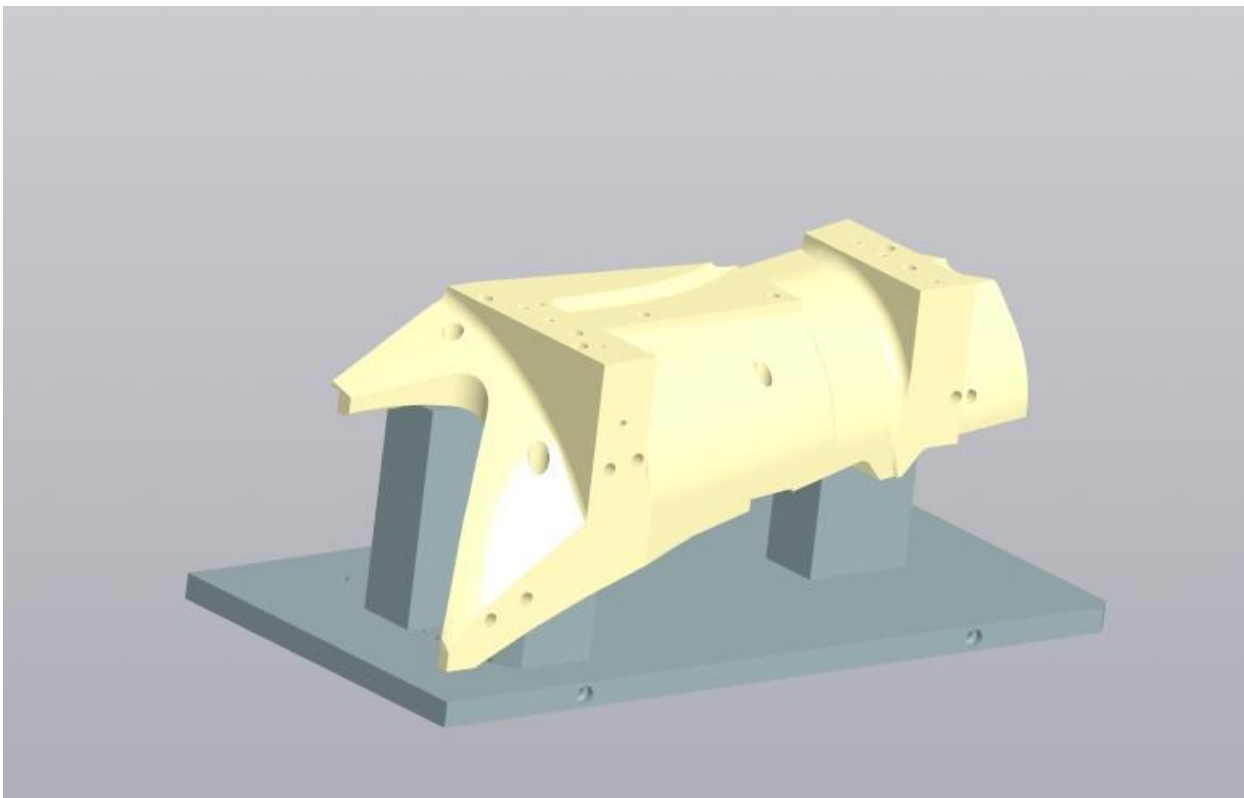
3D-модель установки калибра при чистовой обработке наружной плоскости
